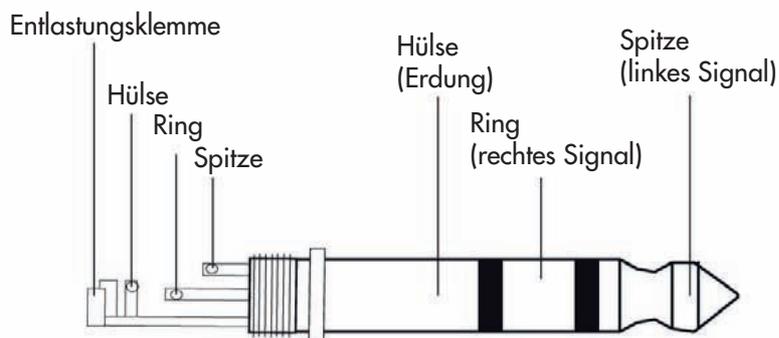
Stereo Stecker für Kopfhörer Verbindung
